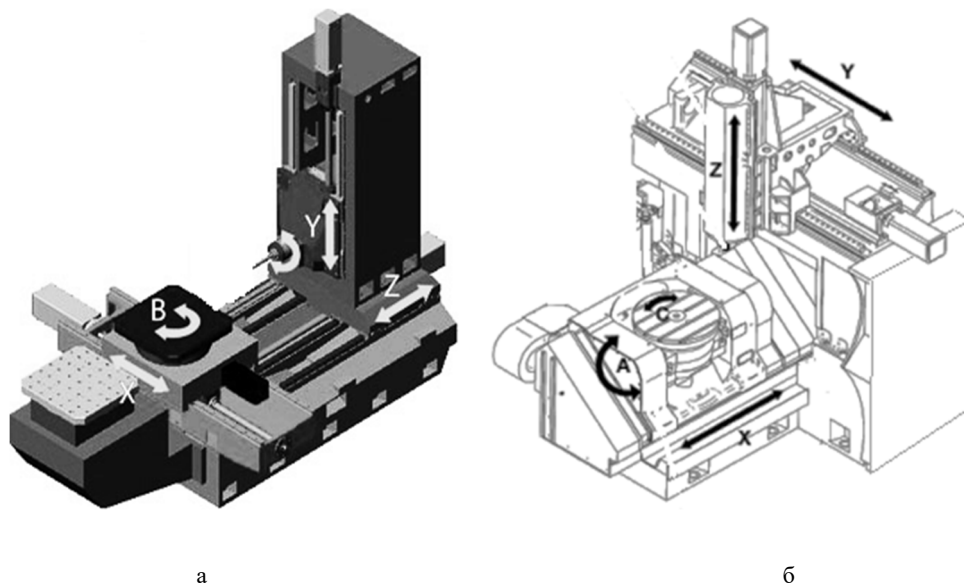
Компонування фрезерних верстатів з ЧПК з обертовими осями
